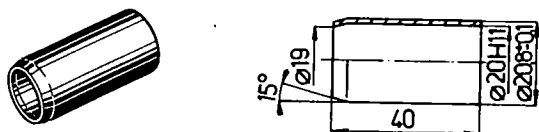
Montáž těsnicího kroužku vedení vysouvací objímky spojky přípravkem MP 3-514
